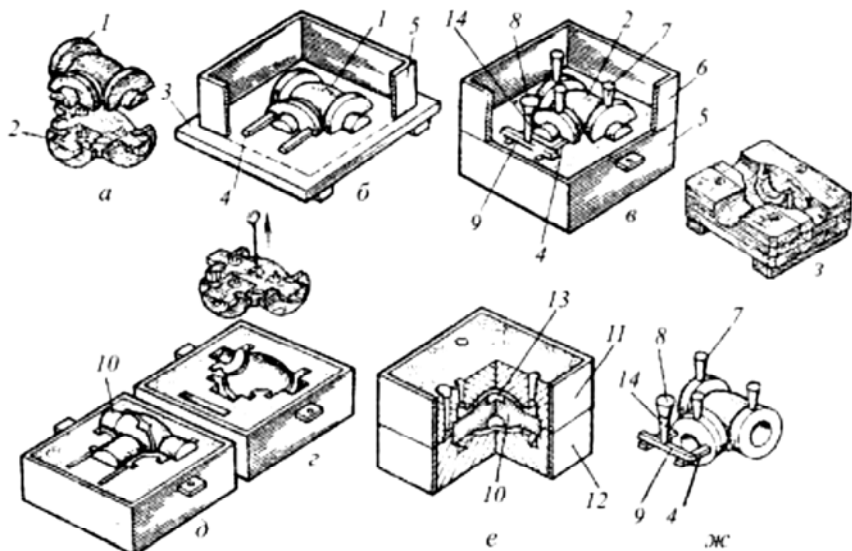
Модель отливки (*а*), отливка «Корпус вентиля» (*ж*) и последовательность изготовления разовой песчаной формы (*б-е*):
